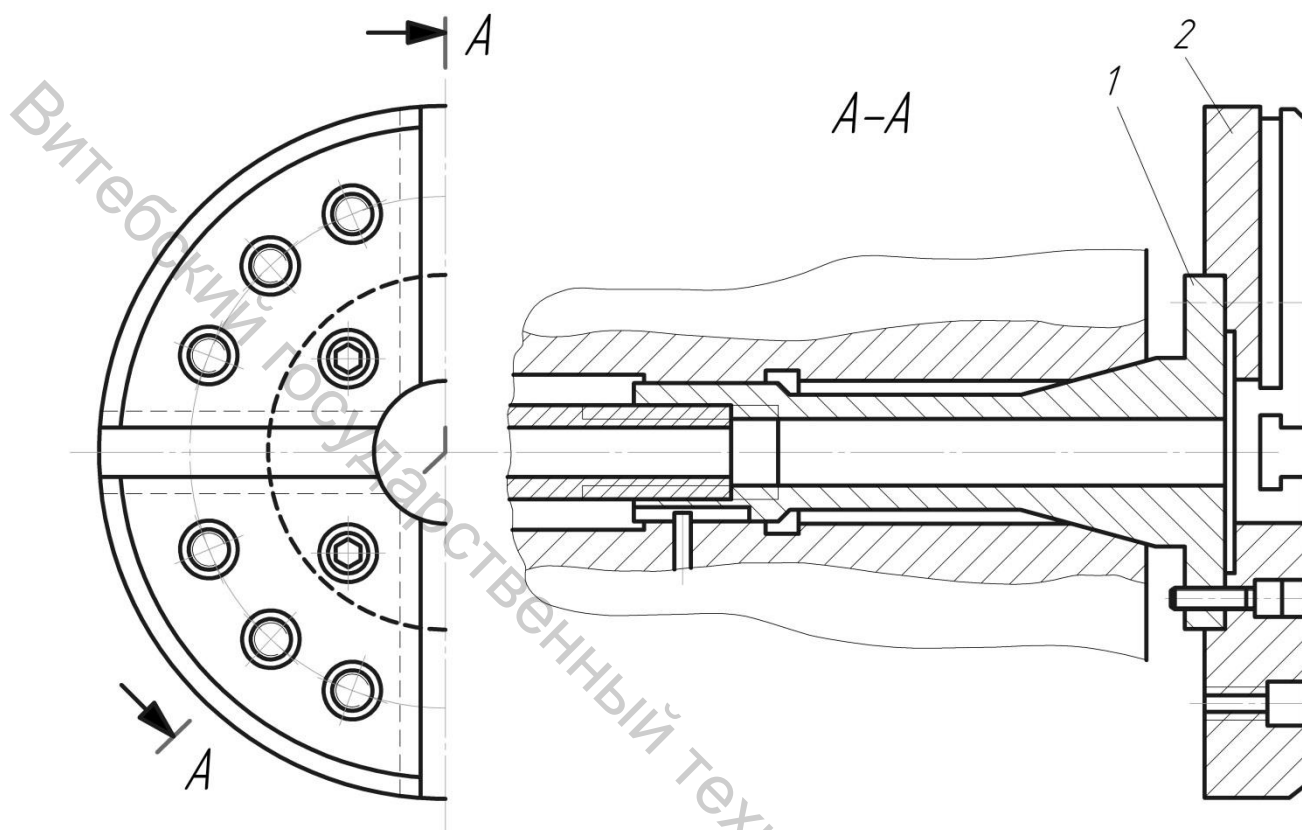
Планшайба универсального круглошлифовального станка для обработки заготовок корпусных деталей
